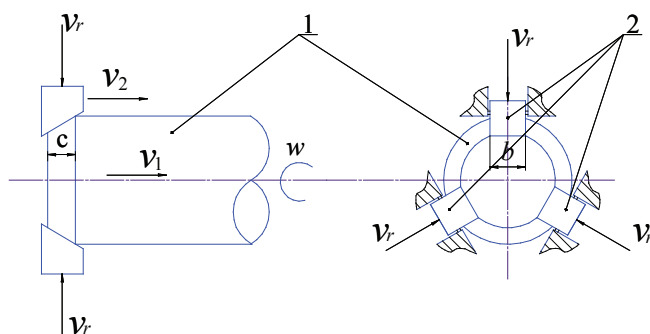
Принципиальная схема обжатия заднего конца заготовки:
